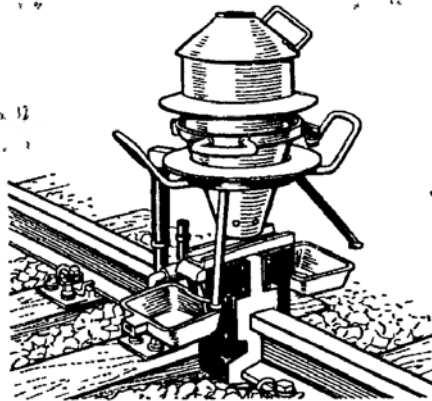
Устройство для термитной сварки рельсов
